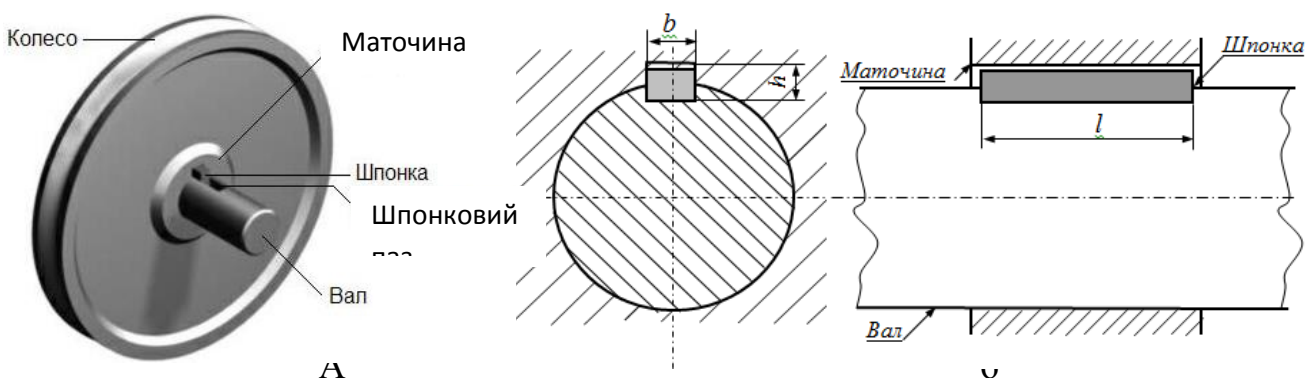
Шпонкове з'єднання: а - деталі; б - зображення
